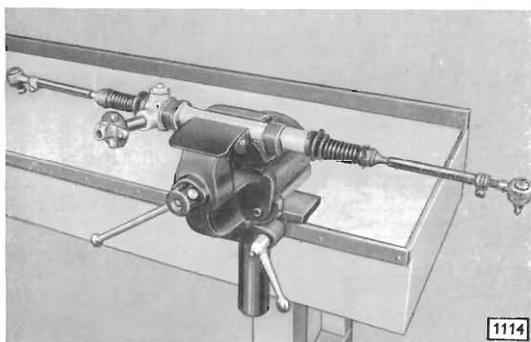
Lenkgetriebe mit Spurstangen im Schraubstock eingespannt
